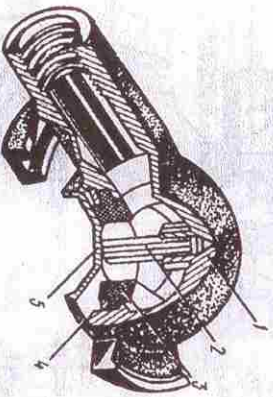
Головка соединительная типа «Б»: 1 — корпус; 2 — сепаратор; 3 — колпачок уплотнительный; 4 — тарелка привода; 5 — крышка
